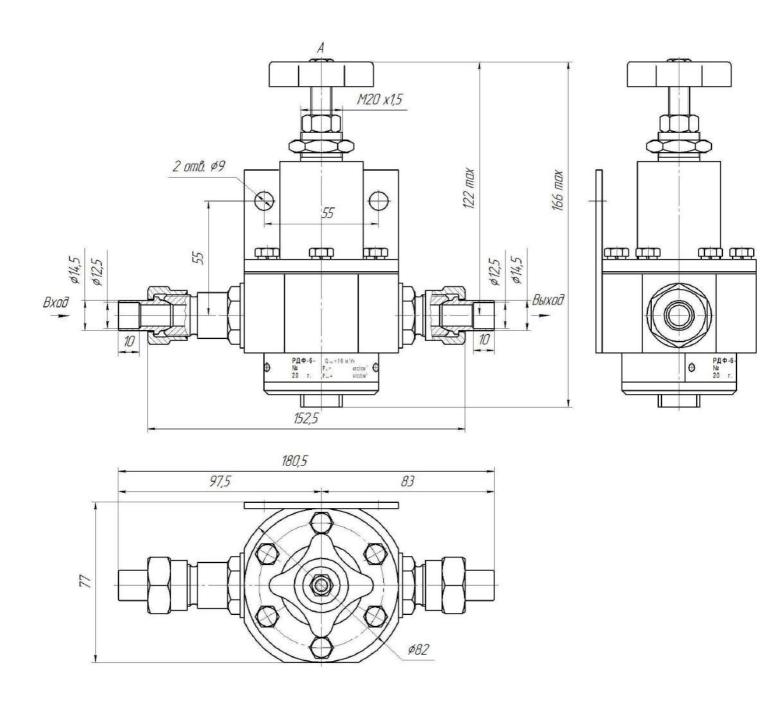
Габаритные и установочные размеры РДФ-6-07
